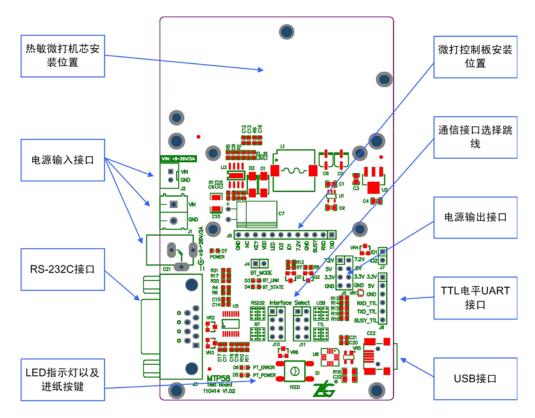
MTP58-FTxx-T1 评估板正面 PCB 丝印
